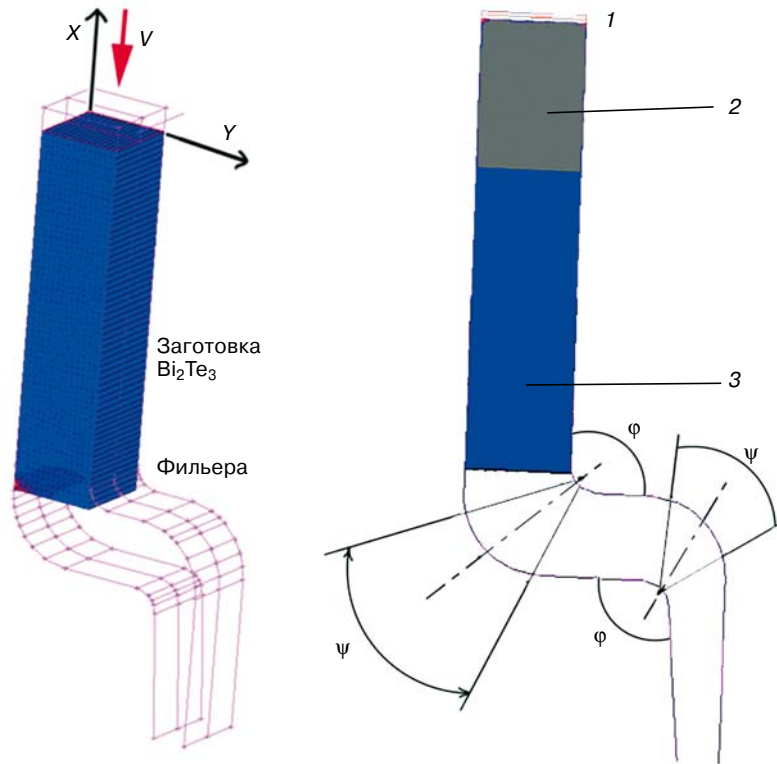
Схема оснастки РКУП: 1 — пуансон; 2 — пресс-шайба; 3 — деформированный образец в процессе РКУП; ϕ , ψ — внутренний и внешний углы соответственно
